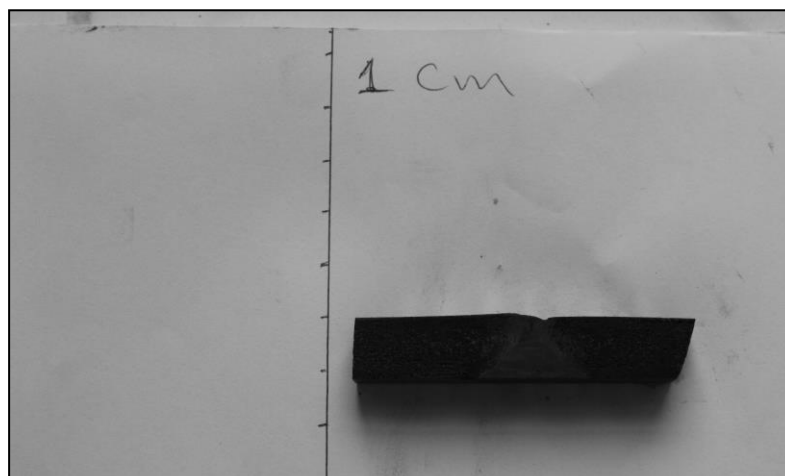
aspect macroscopique de l'acier et son joint soudé sans produits de corrosion H_2SO_4 0.5 M
